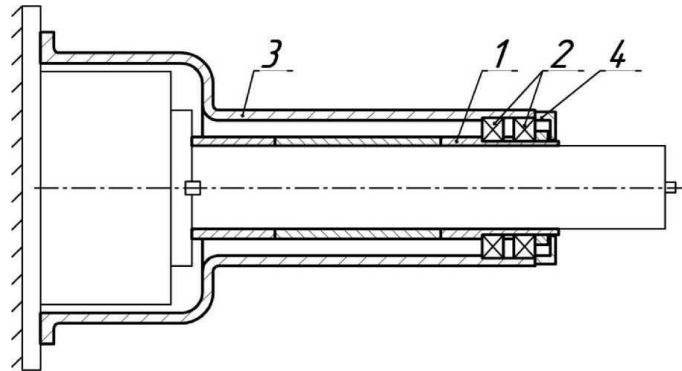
Принципиальная схема устройства для консольного растачивания
